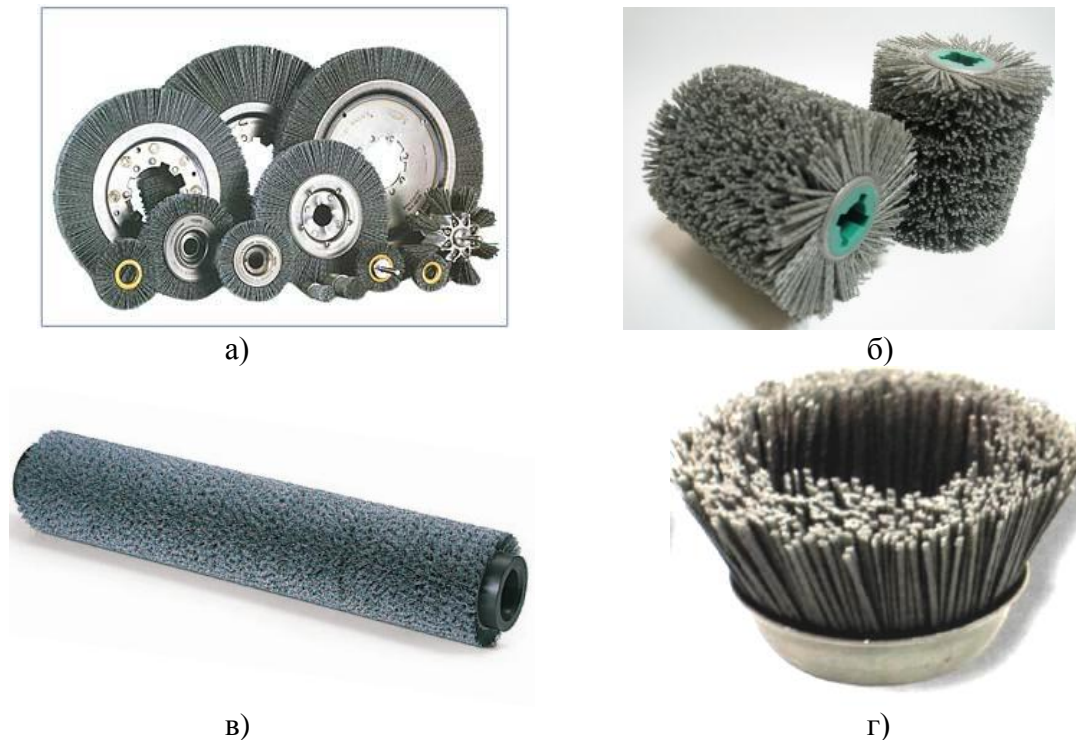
Дисковые а), цилиндрические б), роликовый в), торцевой г) полимерно-абразивные инструменты
